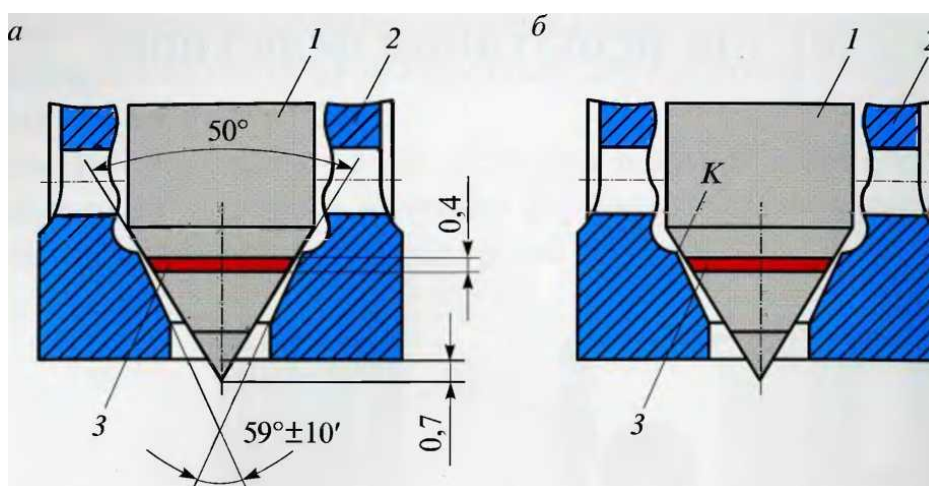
Запорный конус распылителя новый (а) и изношенный (б):
